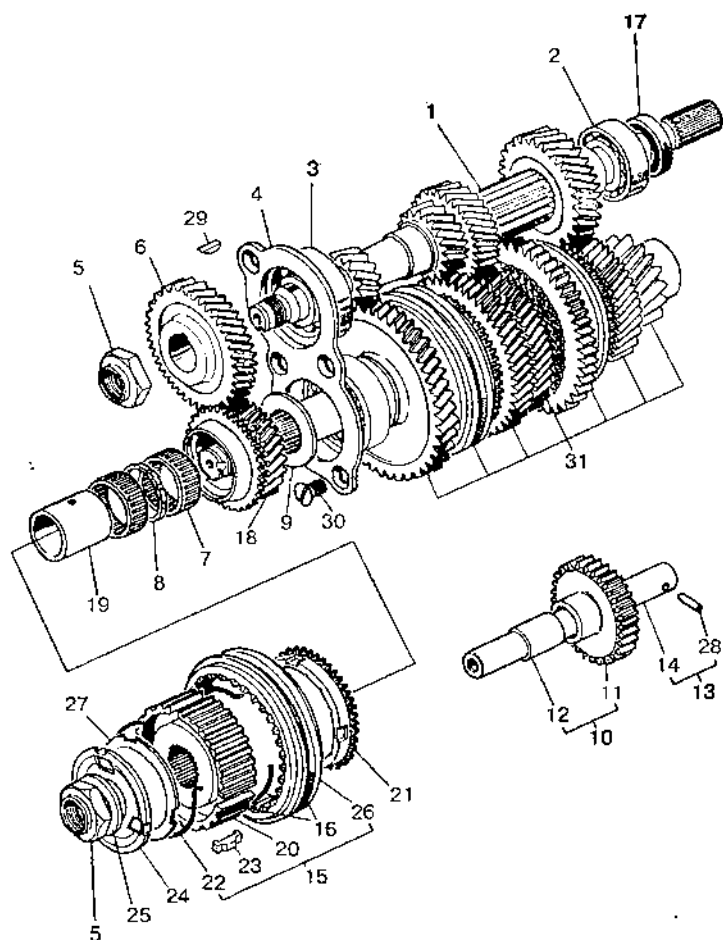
Детали коробки передач (5-я и главная передачи):
